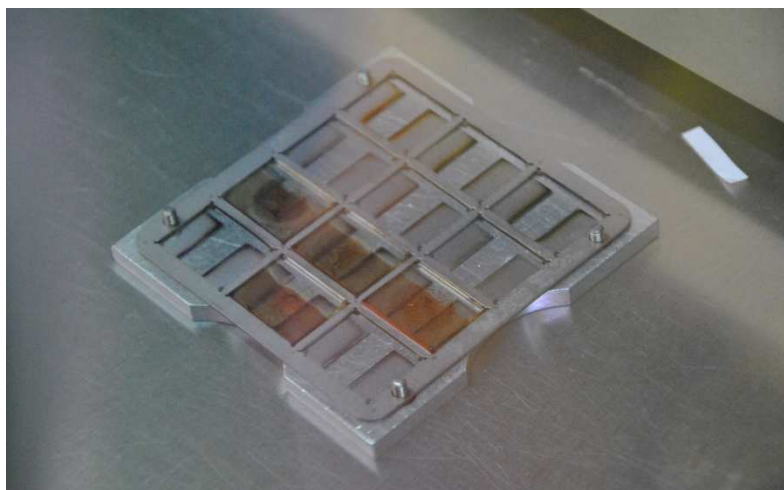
Nanášení PCB vrstvy [vlastní]
